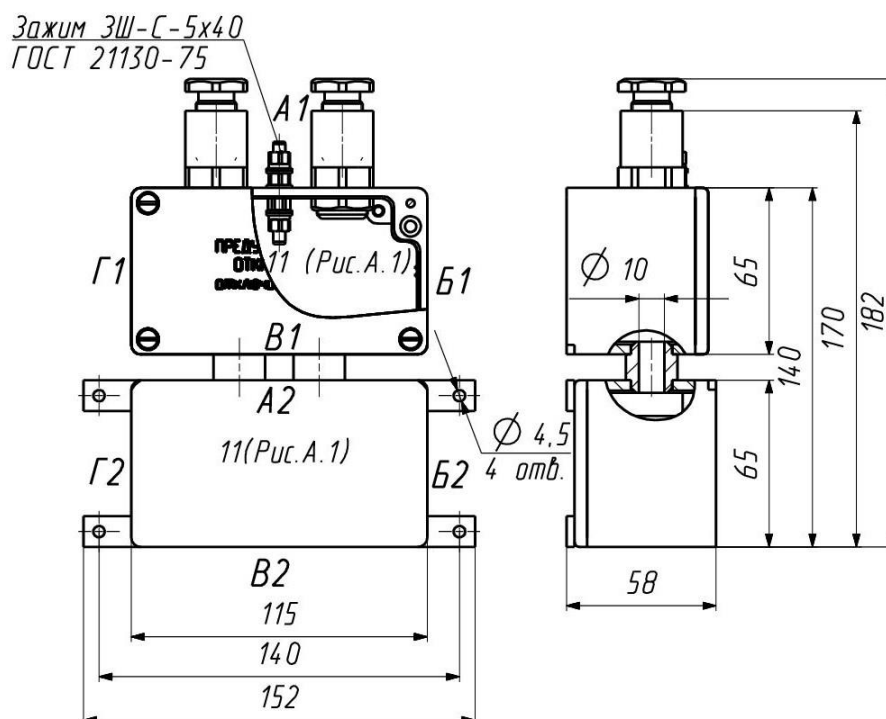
Блок корпусов и коробка клеммная ЕхБКО-А11В1/А11А2 (скрепление двух корпусов типоразмера 11 сторонами В1 и А2) – вариант 6
